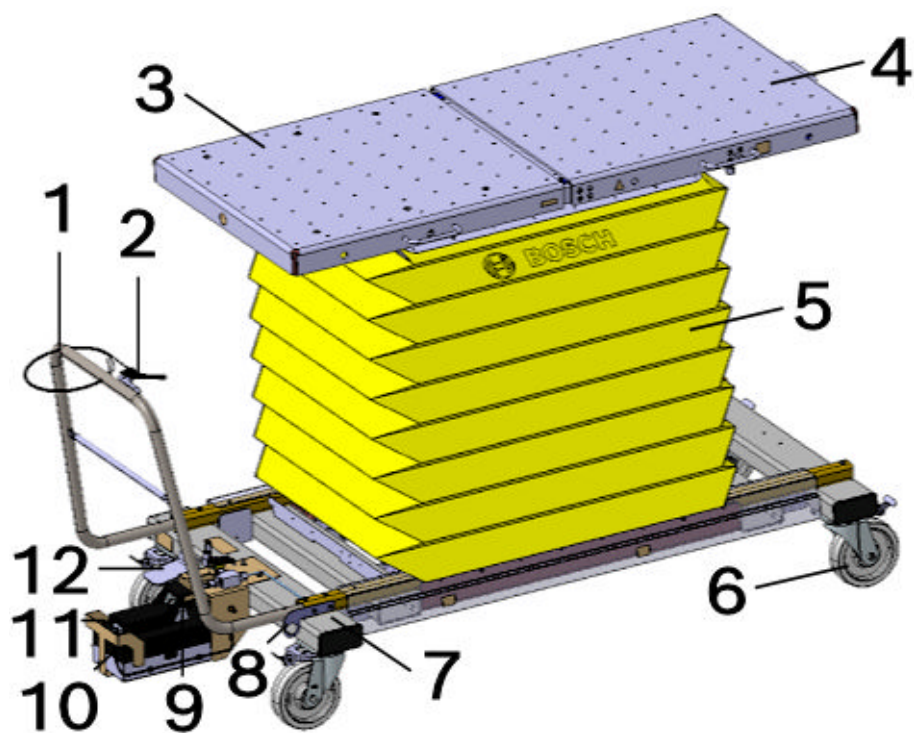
Ножничный подъемный стол 222 3502 022 00
